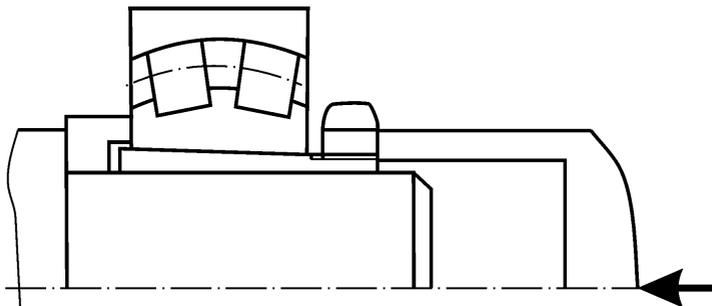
Разборка подшипников с закрепительной втулкой
